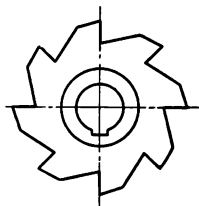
Fräser mit gefrästen Zähnen (spitzverzahnt)
